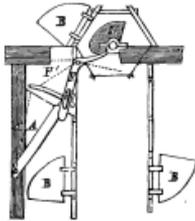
Kubiger's Verbesserung an Elevatoren.
